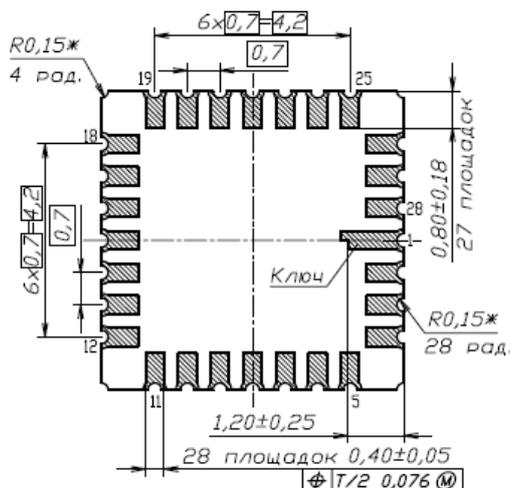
Габаритный чертеж корпуса МК 5123.28-1
